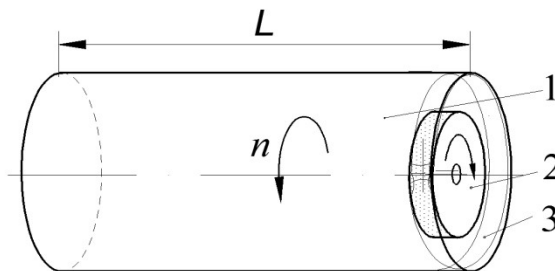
Схема обработки внутренней поверхности цилиндра:
